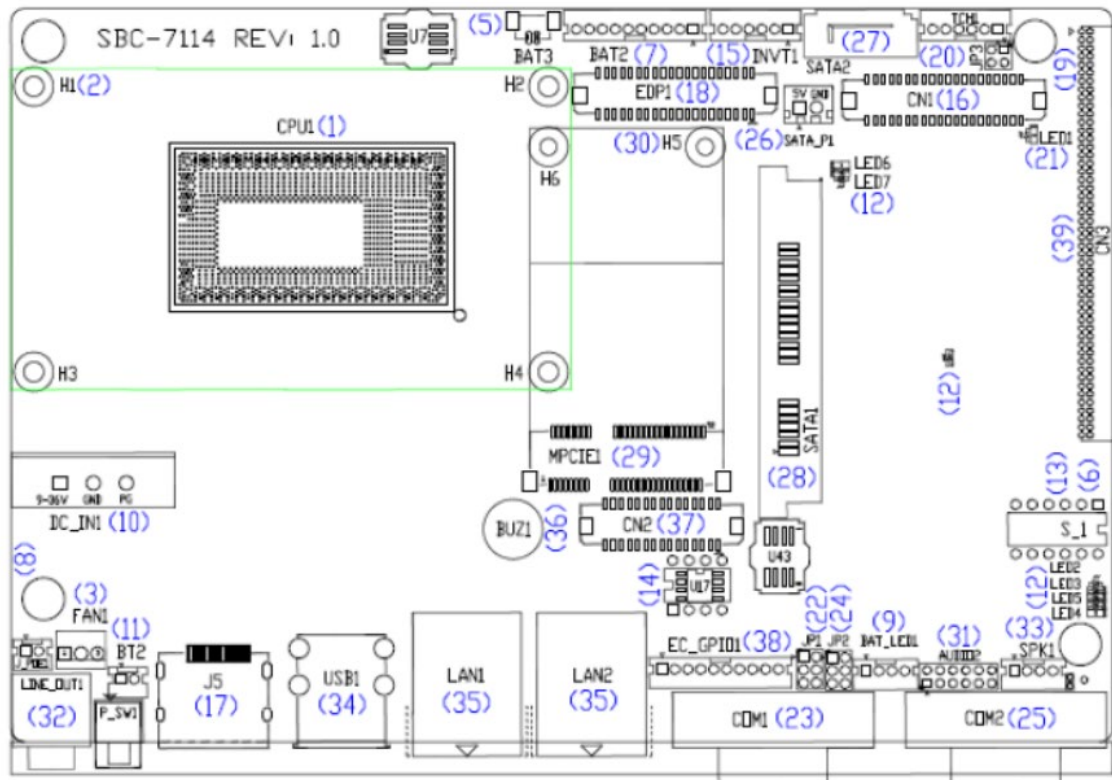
SBC-7114 - Anschlüsse und Jumper - Draufsicht
